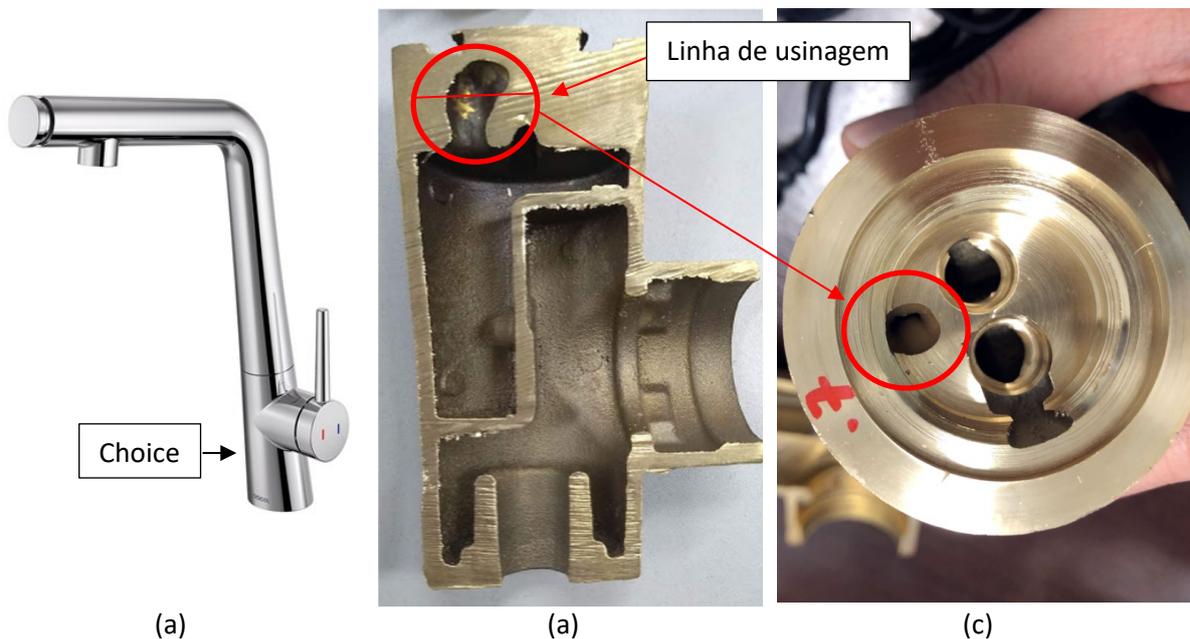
"Choice" (a) Montagem do conjunto, (b) vista em seção do defeito e (c) vista superior após usinagem
